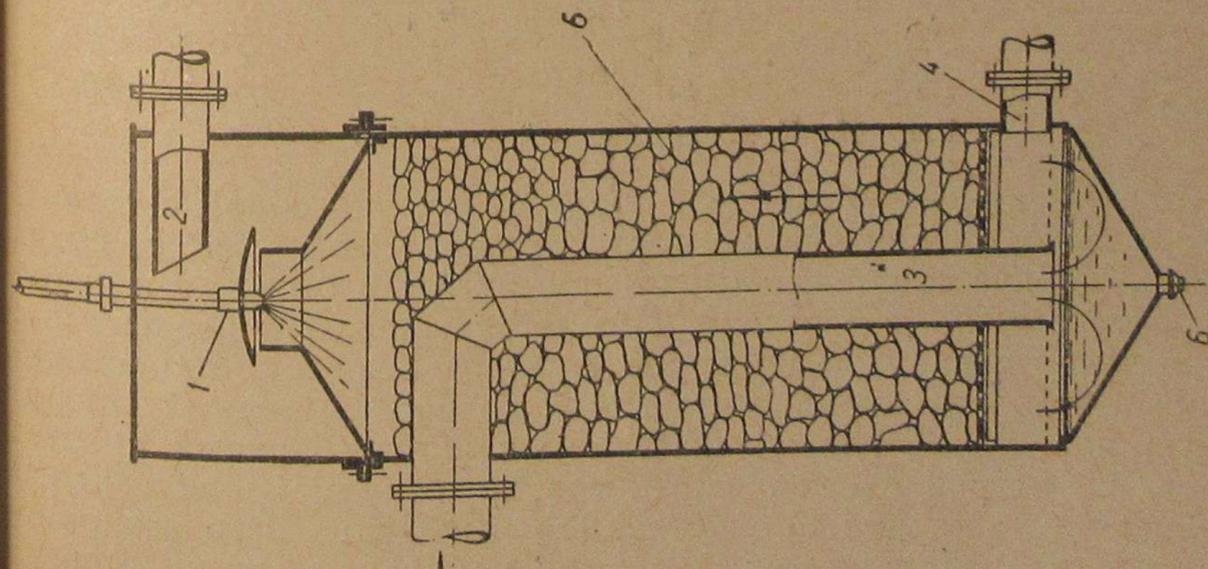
Скруббер типа МСВ-87 с коксовой насадкой
